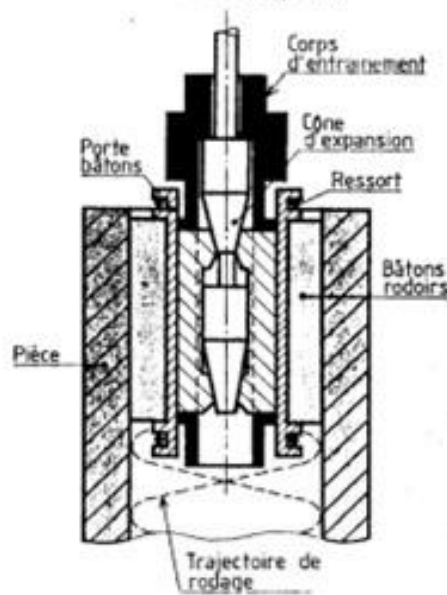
Rodage des surfaces cylindriques intérieures [29]
